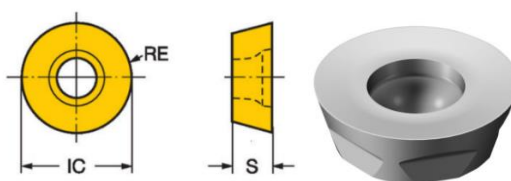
Різальна пластинка з твердого сплаву марки H13A (без покриття) [3]
